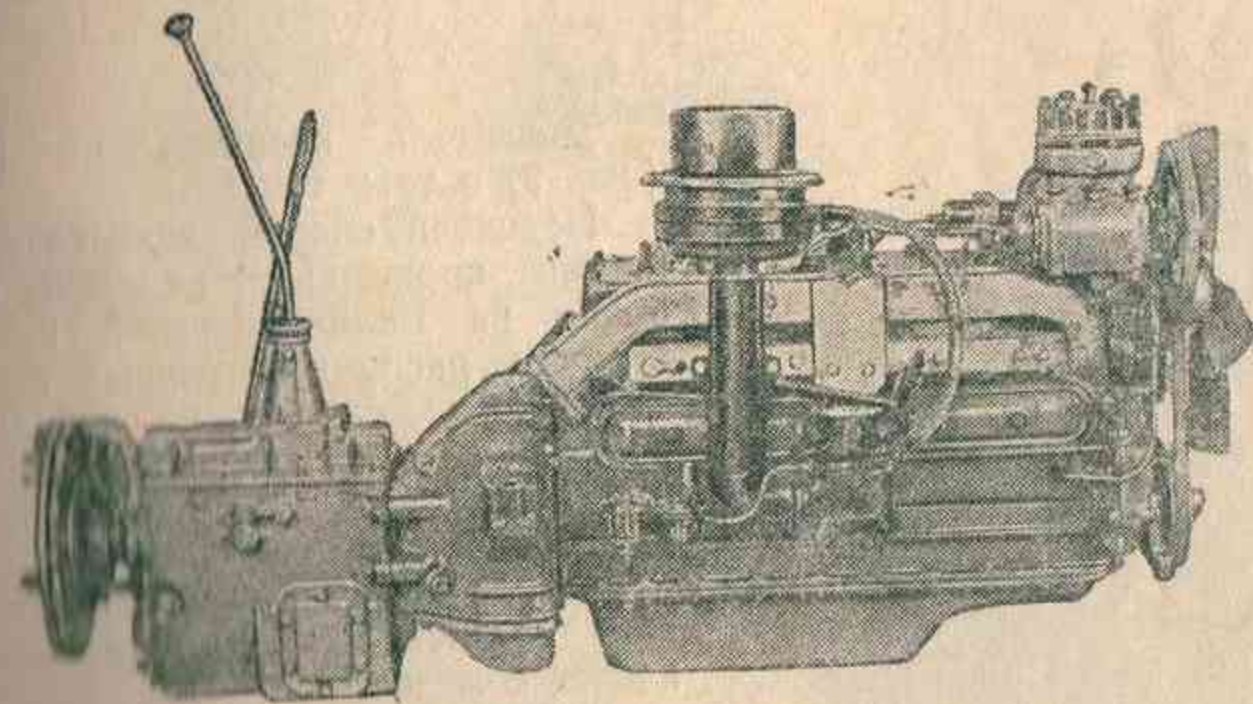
Двигатель со сцеплением и коробкой передач в сборе (вид справа)
